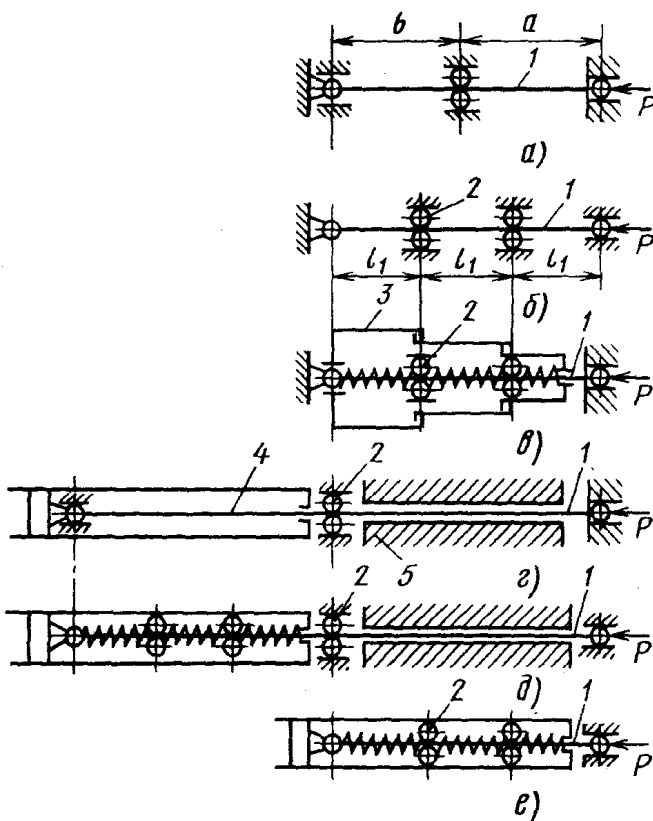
Схеми встановлення свердла для глибокого свердління і з'єднання його з приводом
